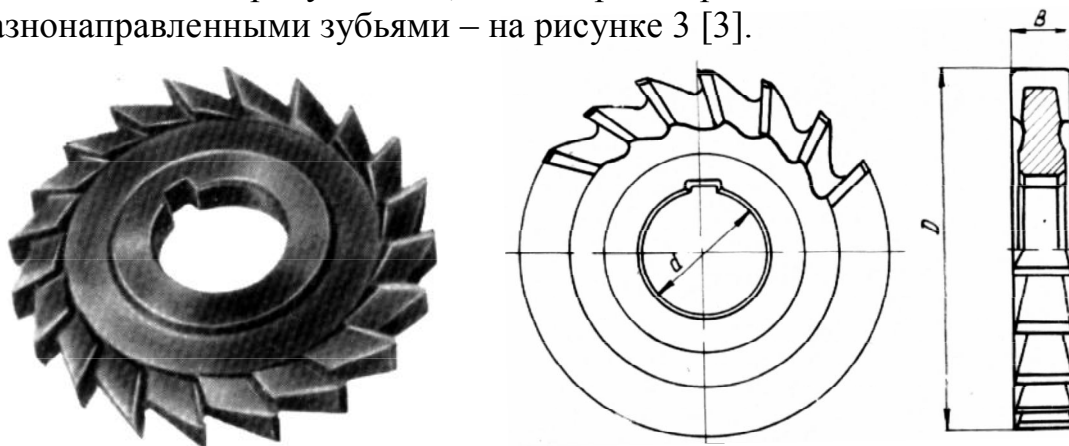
Современная конструкция цельной дисковой фрезы с торцовыми зубьями прямоугольного профиля
